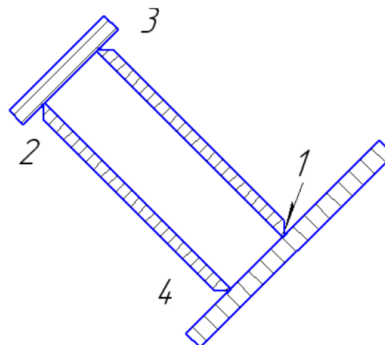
Положення заготовки під час зварювання шва №1
